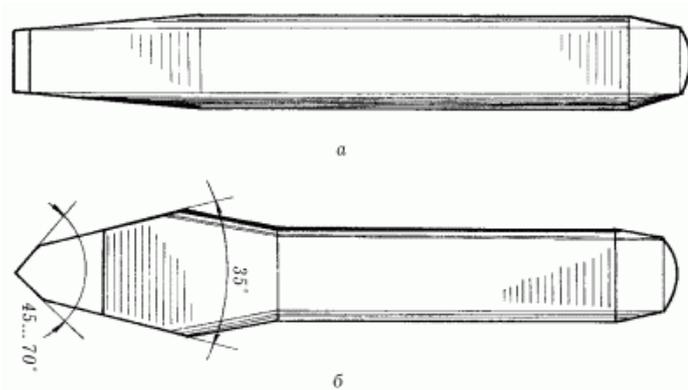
Рубящий инструмент: а – зубило; б – крейцмейсель.
